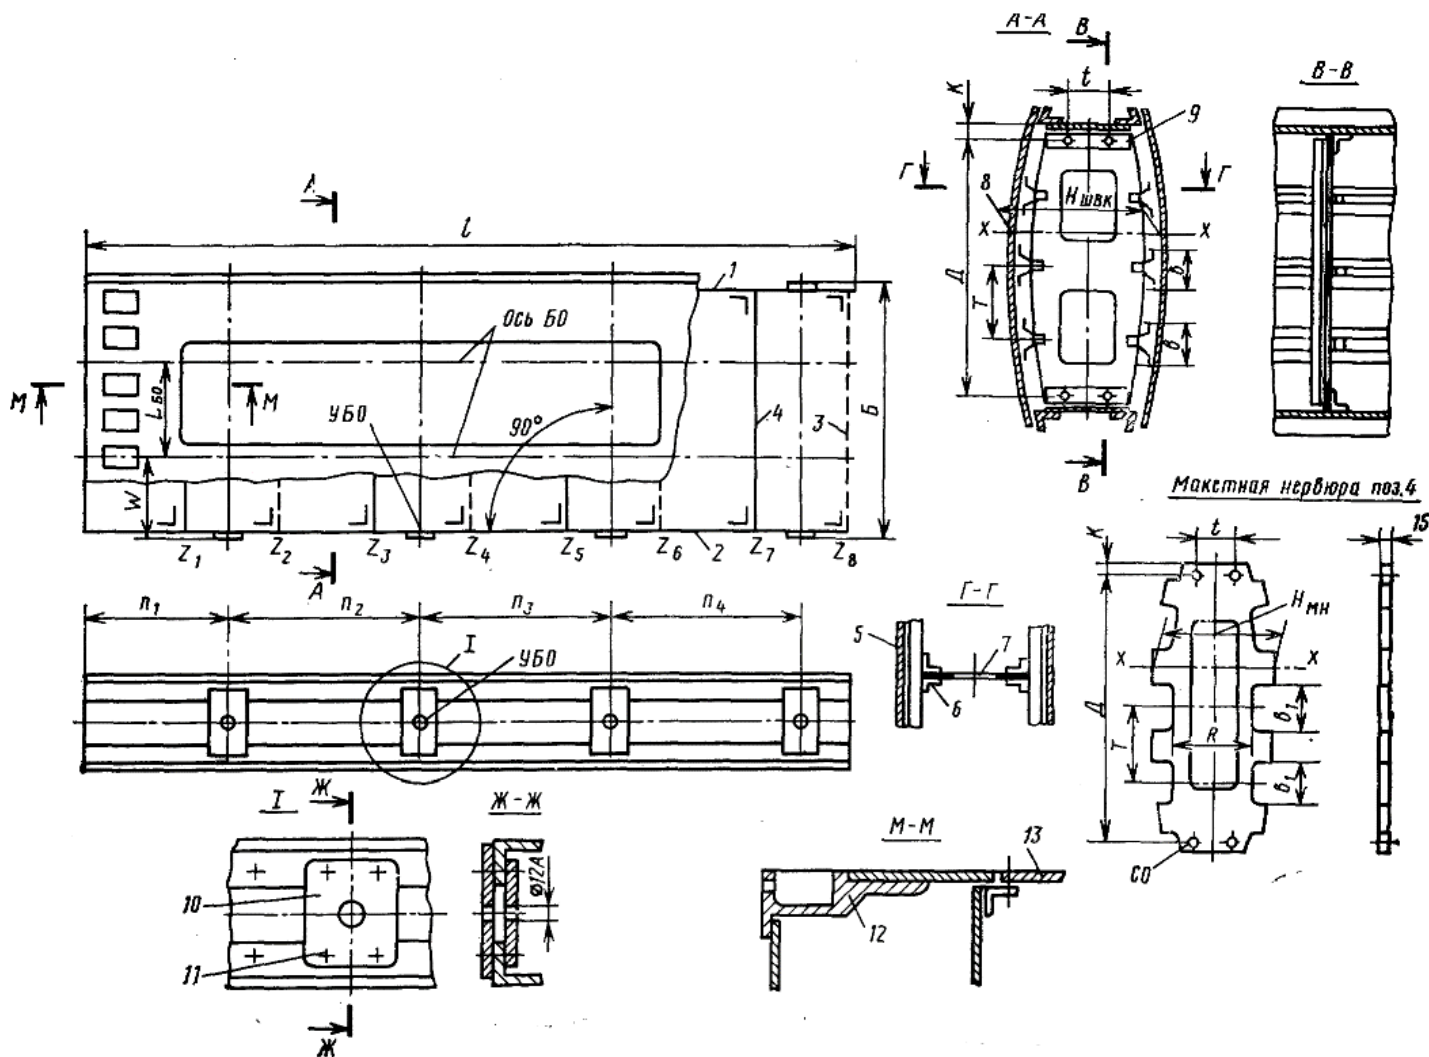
Технологический сборочный чертеж кессона центроплана:
